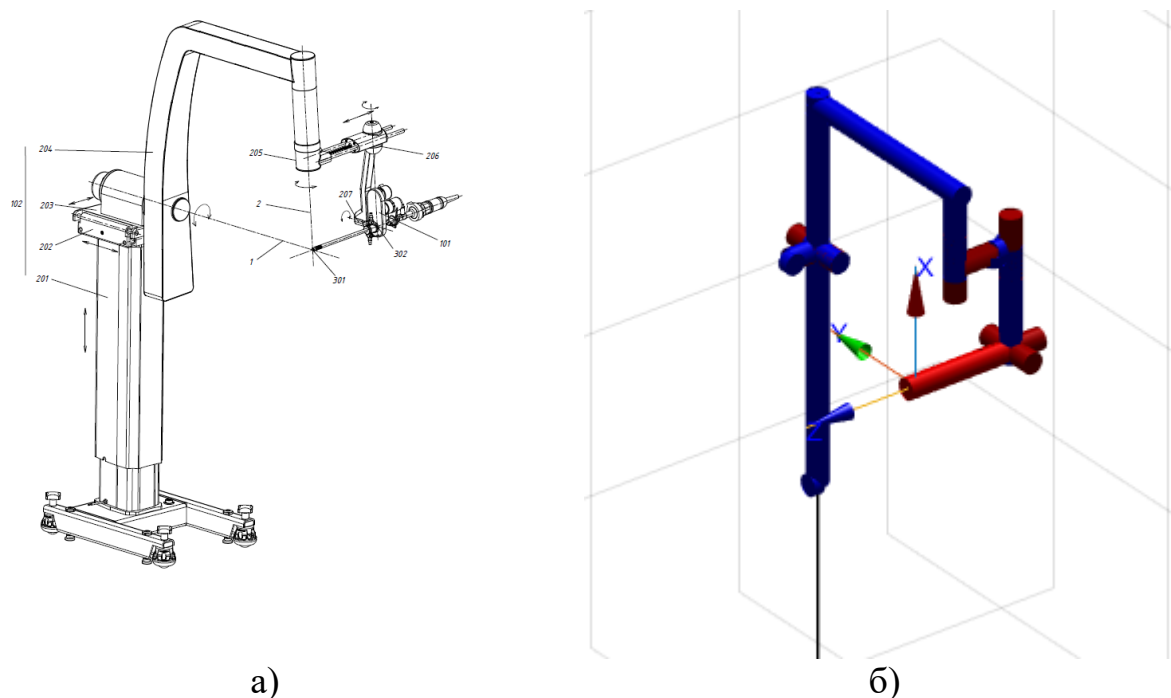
а) Внешний вид конструкции робота; б) кинематическая модель робота в Matlab
